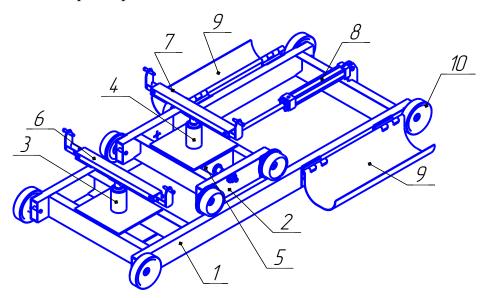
Стенд для расстыковки остова колесных тракторов типа MT3.
